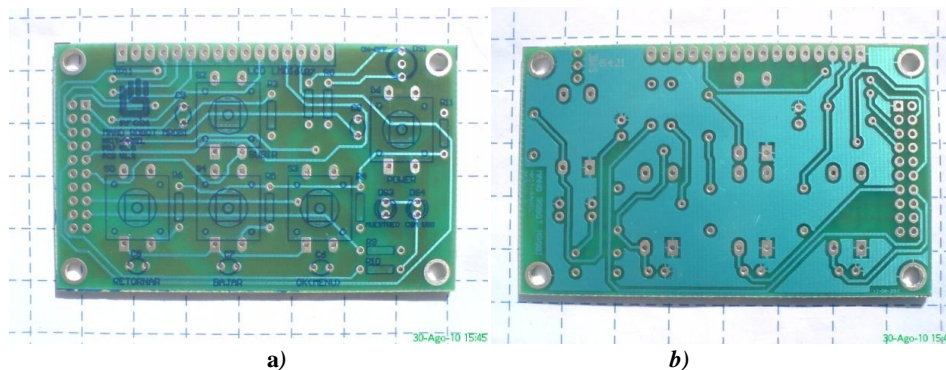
a) Vista frontal la tarjeta PCB fabricada y lista para el montaje. b) Vista posterior.
